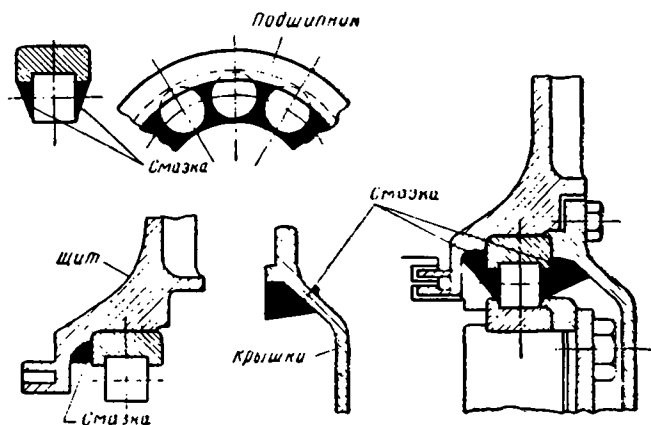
Заполнение консистентной смазкой роликовых подшипников и смазочных камер подшипниковых щитов электрических машин
